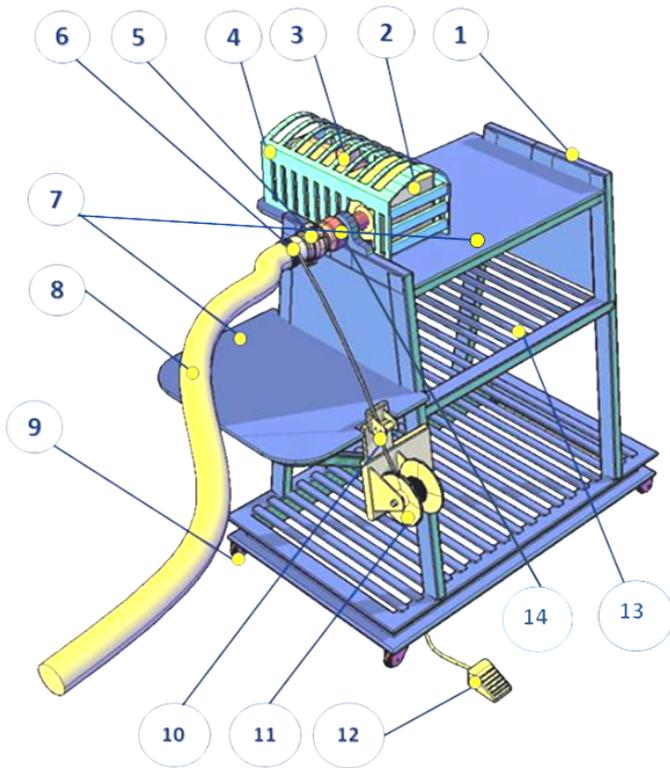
Станок для навязки пожарных рукавов на соединительные головки: 1 — рама; 2 — редуктор червячный; 3 — электродвигатель; 4 — защитный кожух; 5 — полугайки соединительные; 6 — проволока вязальная; 7 — столешница; 8 — рукав пожарный; 9 — колесо-ролик; 10 — ролик направляющий; 11 — кронштейн с катушкой; 12 — выключатель ножной (педаль); 13 — полка; 14 — муфта.
